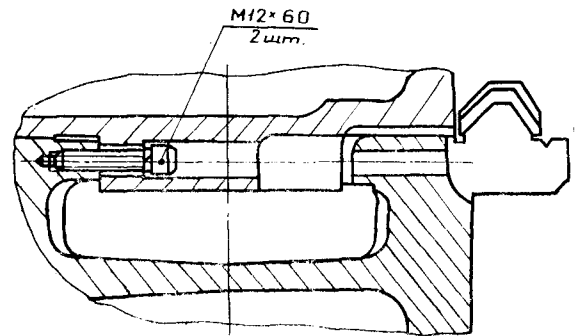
Установка передней бабки (соответственно положению линии центров станка относительно направляющих станины)
